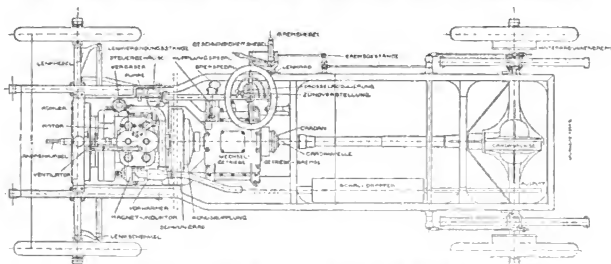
Zweizylinder-Cardanautomobil mit 1 Cardangelenke, gebaut von der N. A. O.
